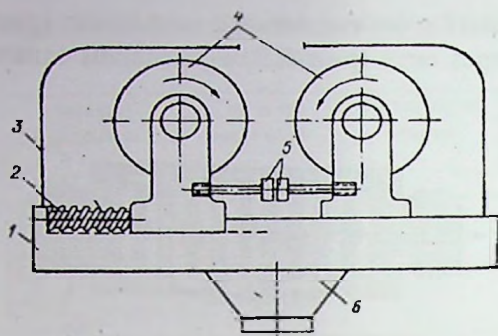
Дробилка с гладкими валками для среднего дробления:
